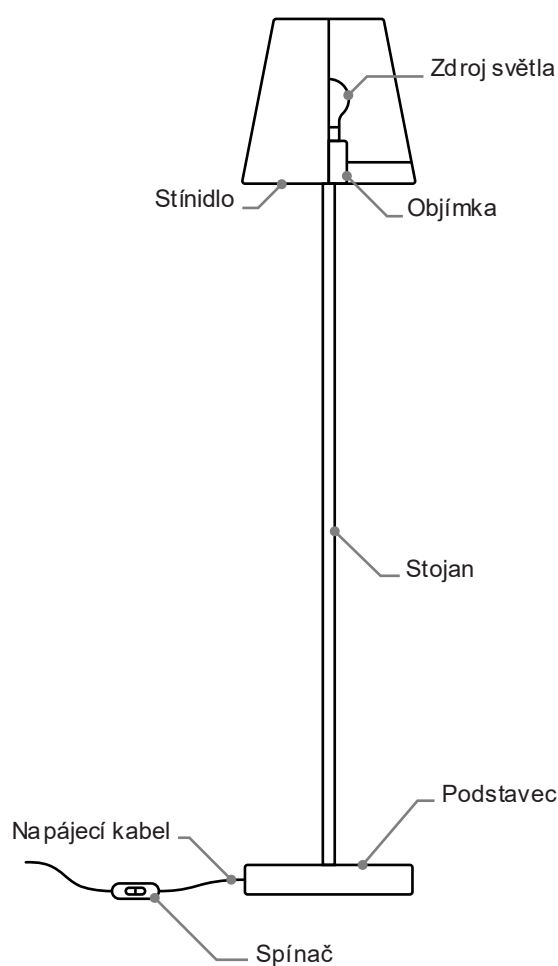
Stojací lampa Luceplan Levante Floor[10]
